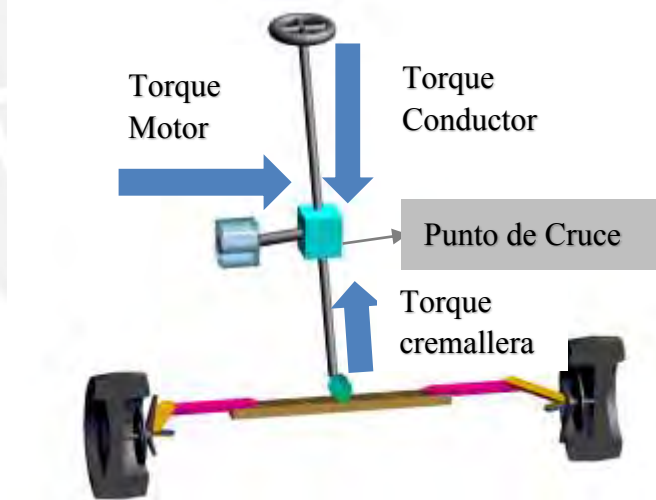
Cross-Checking del Sensor Par de Torque [Adams/View]
